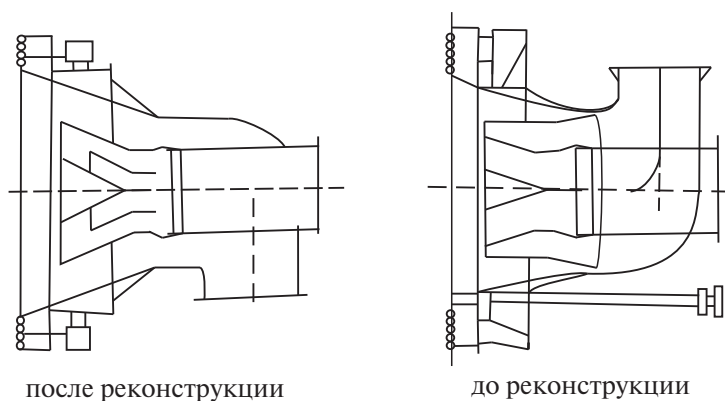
Установка горелки в корпусе котла ПК-33
